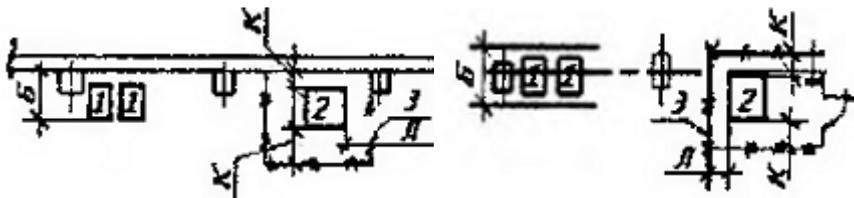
Размещение оборудования для сварки длиномерных деталей: 1 - рольганг для подачи труб; 2 - установка для сварки труб; 3 - накопитель.
